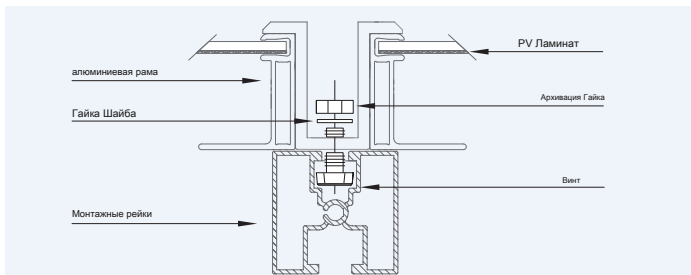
Деталь сверху вниз зажим крепления монтажной
